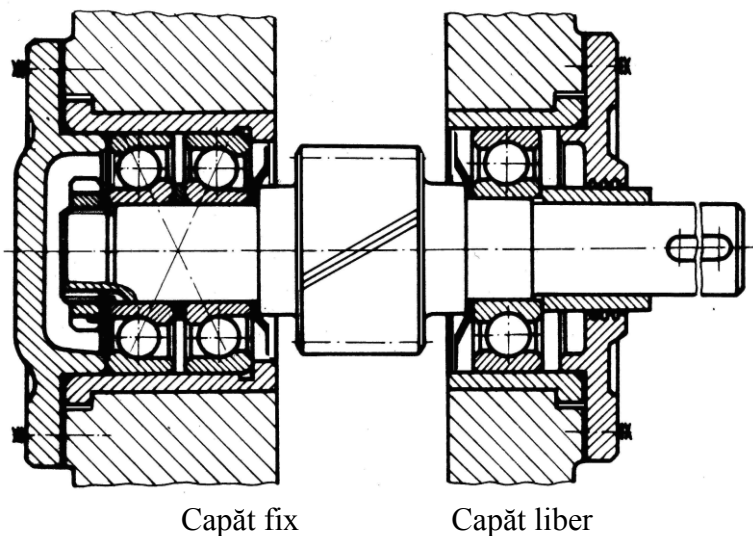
Montaj cu fixare axială la un singur capăt, cu doi rulmenți radial-axiali cu bile și un rulment radial cu bile
